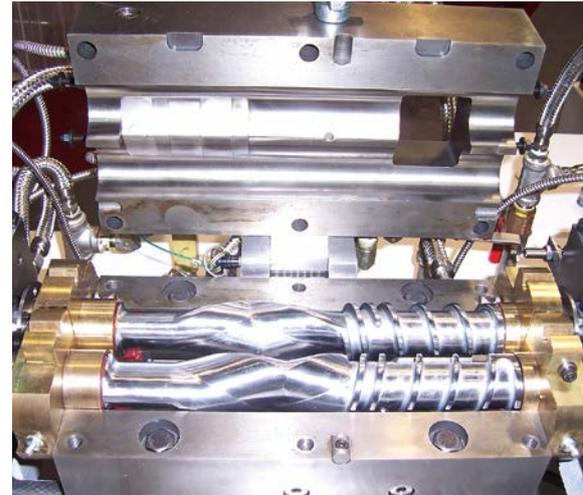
Geöffnete Mischkammer mit beidseitig gelagerten Rotoren und Segmenten in der oberen Kammerhälfte (Bild: Farrel Pomini)
